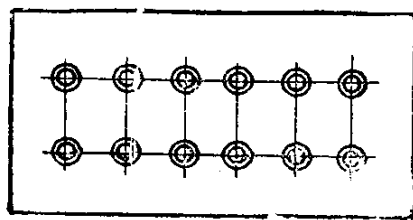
Накладной кондуктор, устанавливаемый по габаритным размерам.
